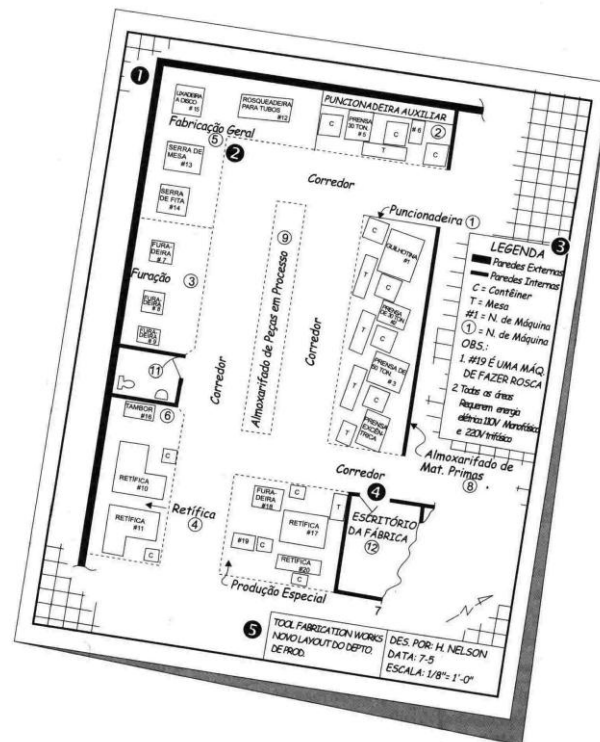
Plano Detalhado de Leiaute do SLP Simplificado
